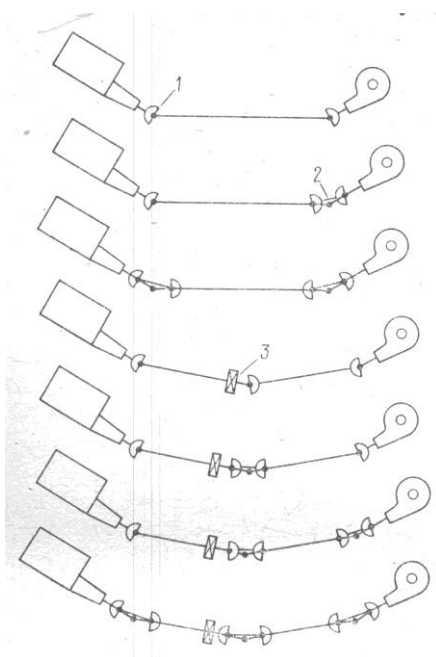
Конструкция приводного вала легкового автомобиля. 1 – универсальный карданный шарнир; 2 – двойной универсальный карданный шарнир; 3 – опорный подшипник вала.
